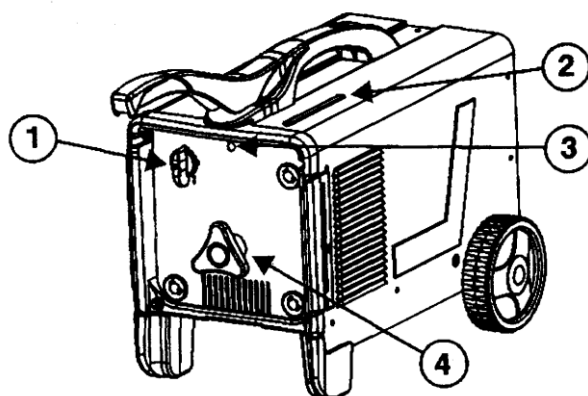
Сварочный аппарат GAMMA 3250:
